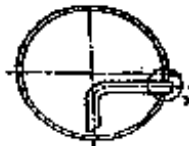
Tube plongeur fixé à la visière d'un récipient horizontal
